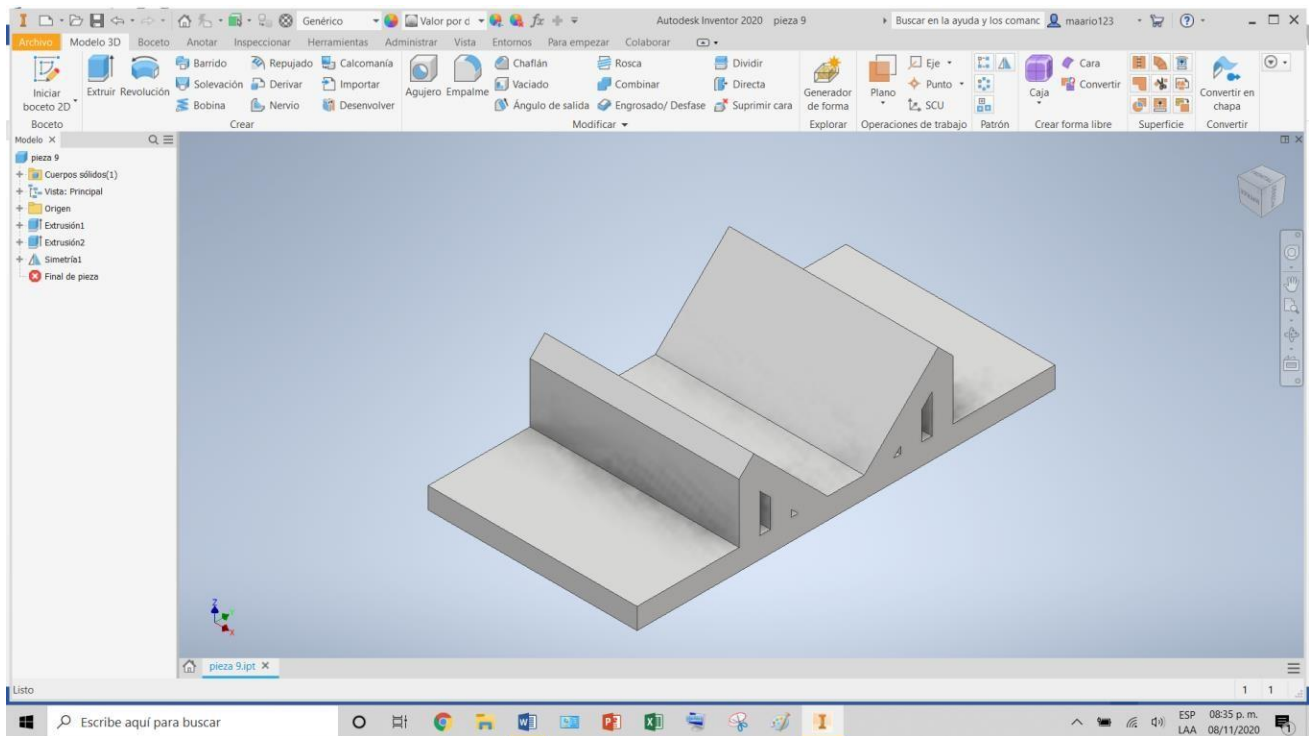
Diseño 3D de molde para troquelado parte inferior.
